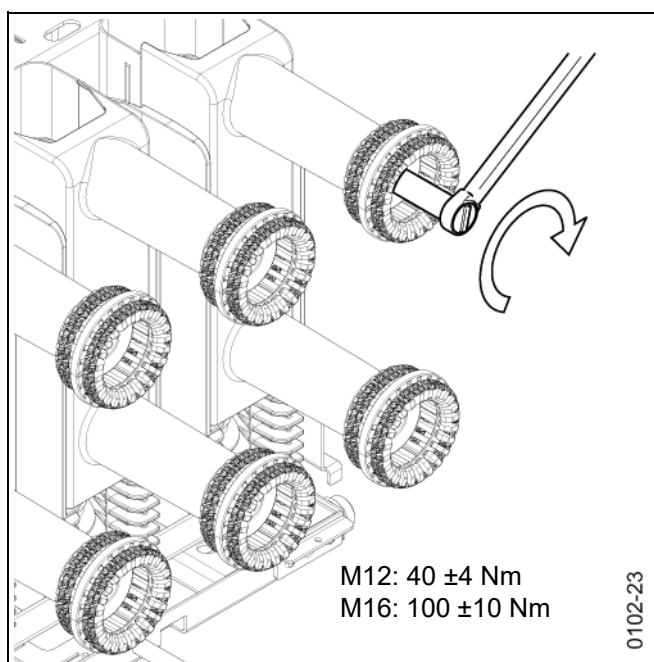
Kompletowanie systemu styków 2000 A (widok przekrojowy)
